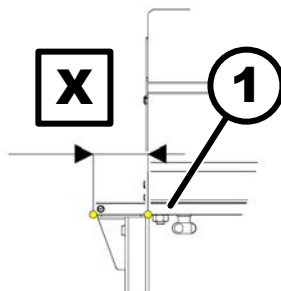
Detalle - Posición de montaje del carro escuadrador
